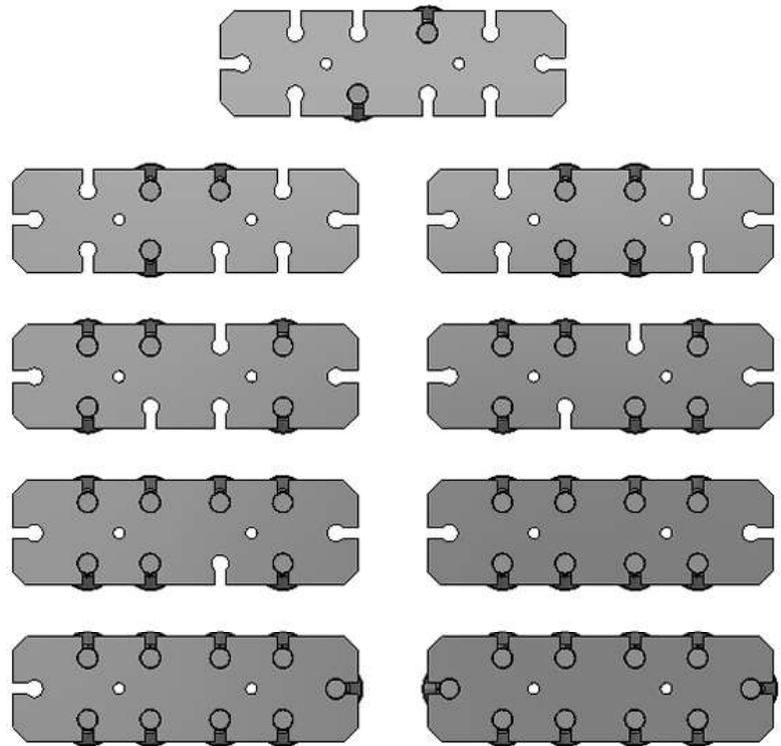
Plan de disposition pour les barrières ACCESSPARK-4500
